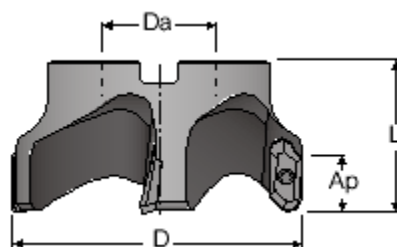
Těleso frézy pro hrubování hliníku s povlakem GOLDALU. [28]
